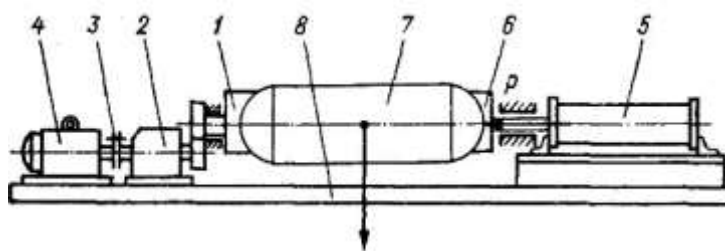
Двухстоечный кантователь с торцевыми планшайбами
